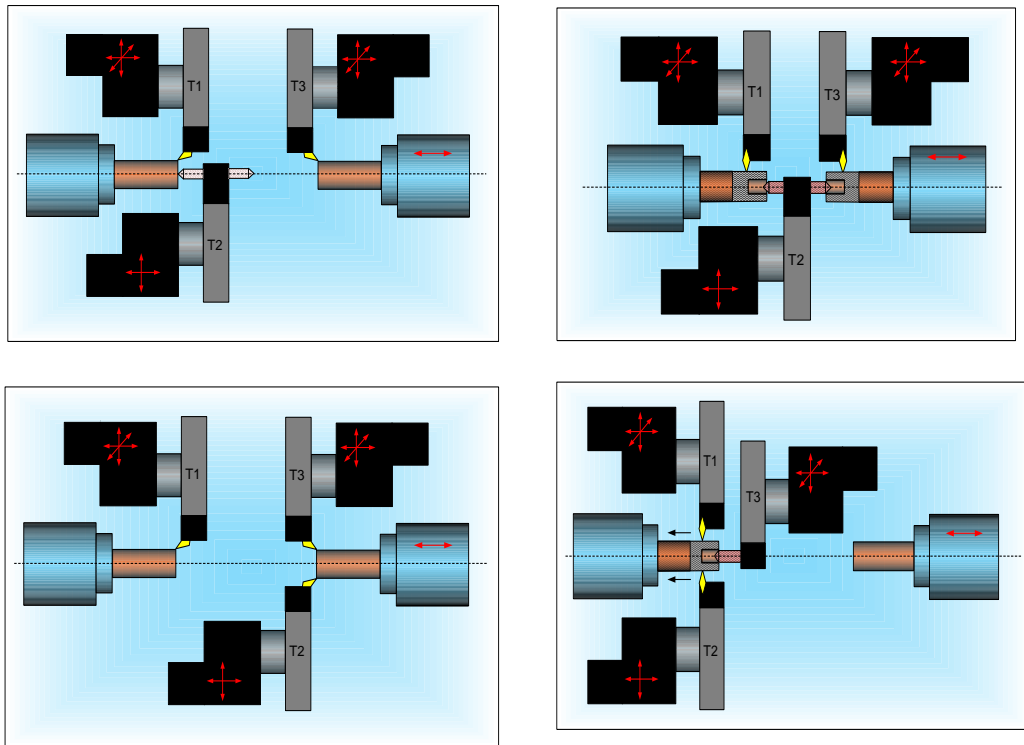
Схеми обробки на токарних верстатах з трьома РГ
